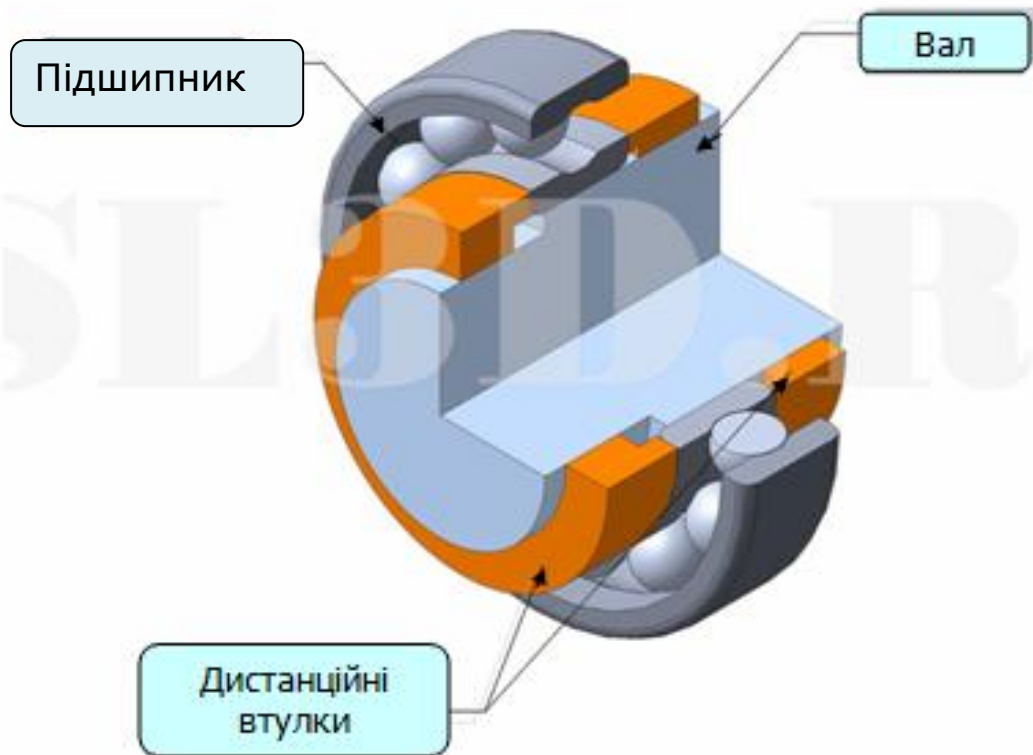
Установка підшипника з затягуванням між дистанційними втулками
